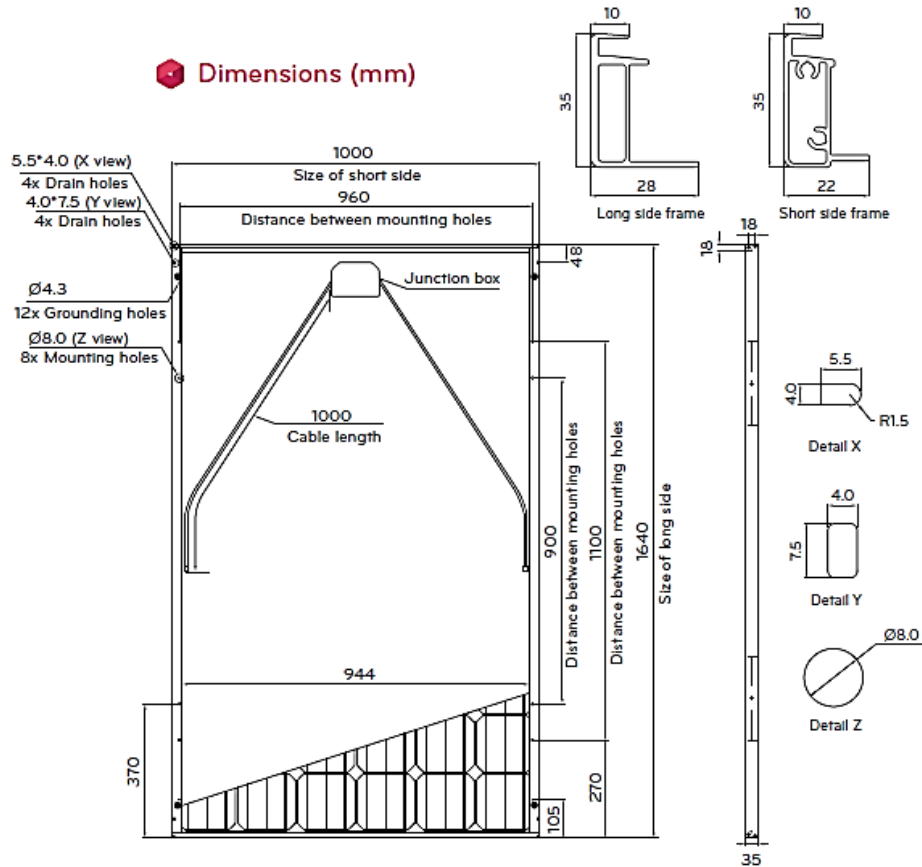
Dimensiones del panel solar fotovoltaico LG Electronics 255S1C-G3
